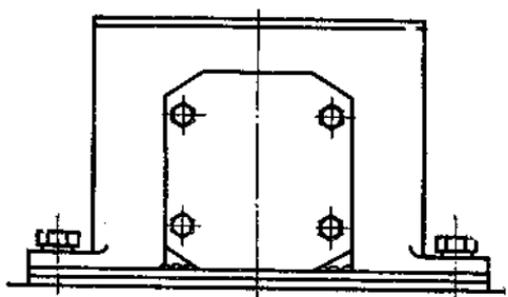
Походное положение крышки защиты головки ночного прицела ТПН1-49-23
